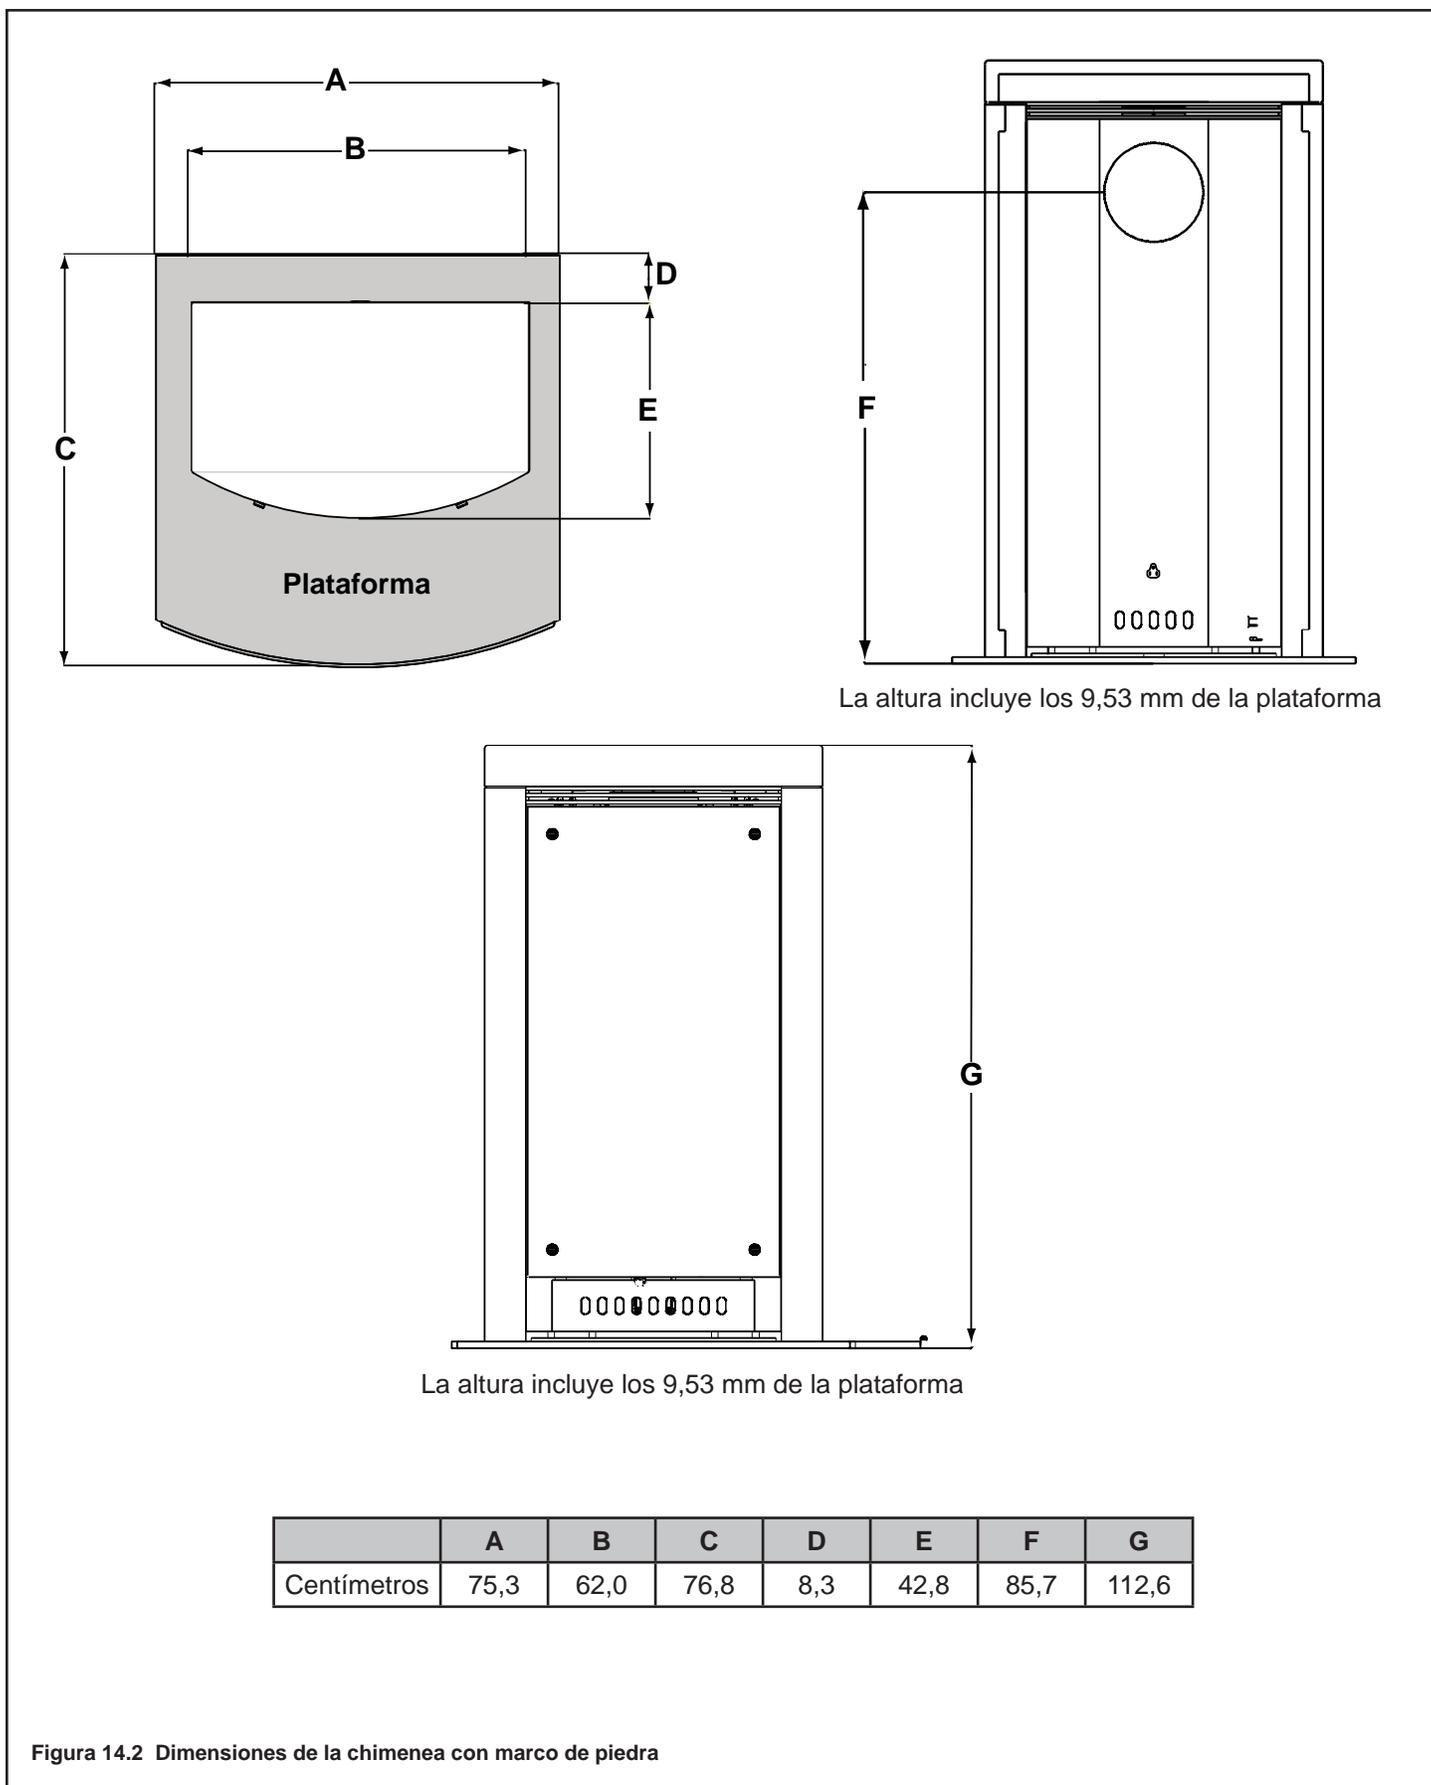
Dimensiones de la chimenea con marco de piedra
